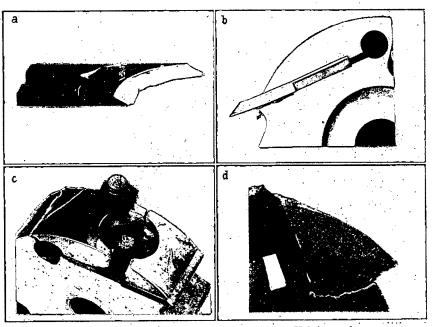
d. Unfallursachen bei zusammengesetzten Holzfräswerkzeugen.
